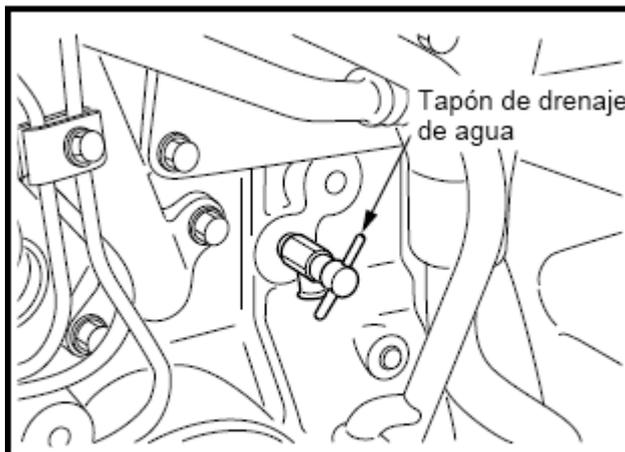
Tapón de drenaje de refrigerante (motor)
